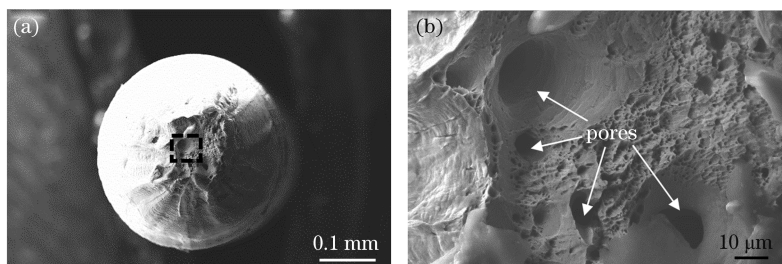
Cu 100 焊接接头的断口形貌。(a) 断口形貌; (b) 图(a)的局部区域放大
